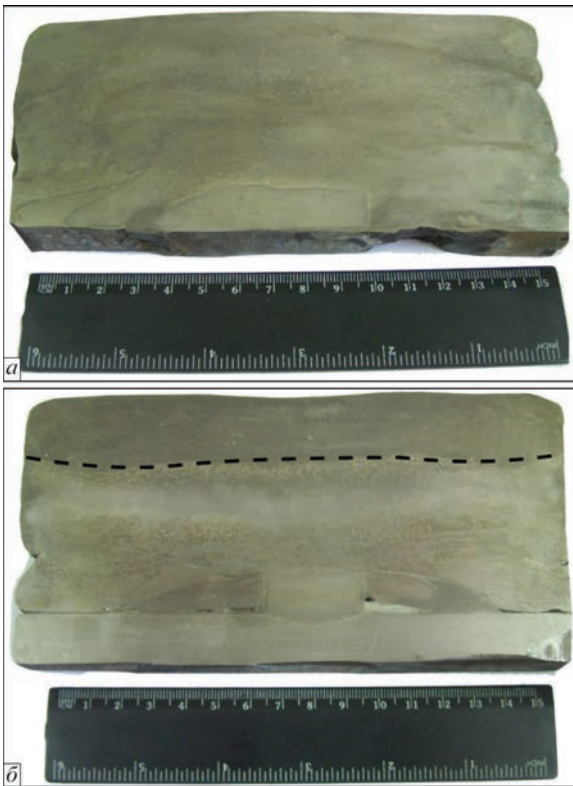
Продольный макрошлиф биметаллической заготовки, полученной наплавкой электродом диаметром 90 мм при $N_{\text{ТПК}} = 80...90$ (а) и $130...135$ кВ·А (б) (штриховой линией обозначена форма металлической ванны в наплавленном металле)
